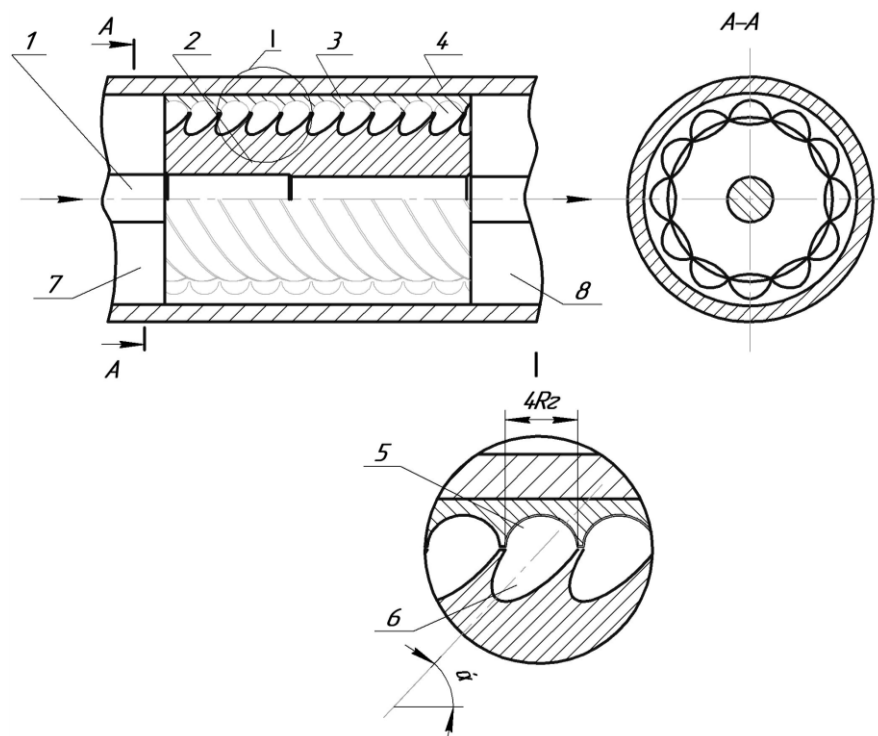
ЛГН з удосконаленою формою робочих органів: 1 – привідний вал; 2 – гвинт; 3 – втулка; 4 – корпус; 5 – гвинтова канавка втулки; 6 – гвинтова канавка гвинта; 7 – фаска біля вихідної порожнини; 8 – камера підведення; 9 – камера відведення
